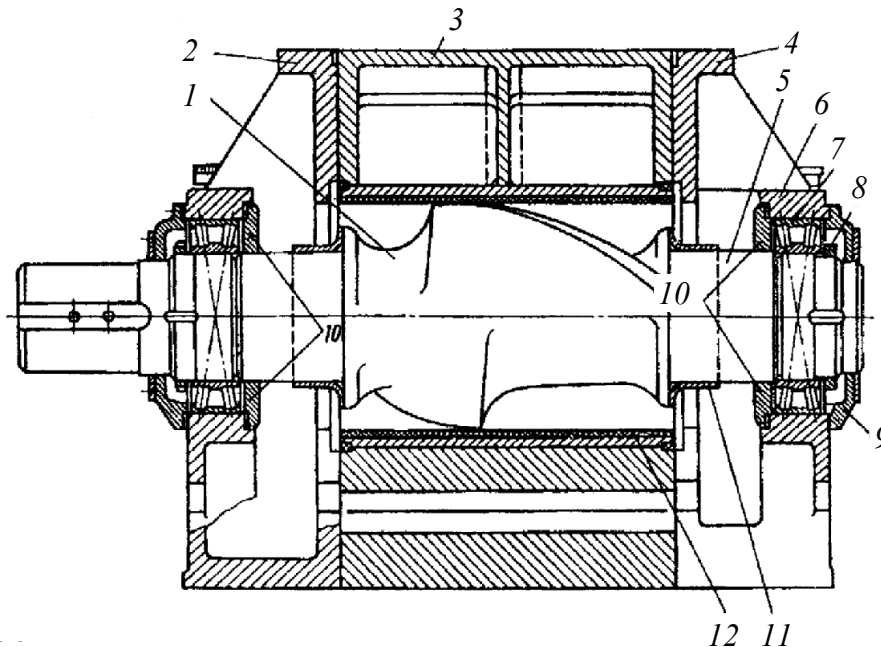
Розташування овального ротора в робочій камері змішувача: 1 – ротор; 2, 4 – бокові стінки камери; 3 – корпус змішувальної камери; 5 – шийка ротора; 6 – корпус підшипника; 7 – підшипник; 8 – гайка; 9 – кришка підшипника; 10 – ущільнення; 11 – ущільнювальна втулка; 12 – внутрішній зносостійкий покрив камери
